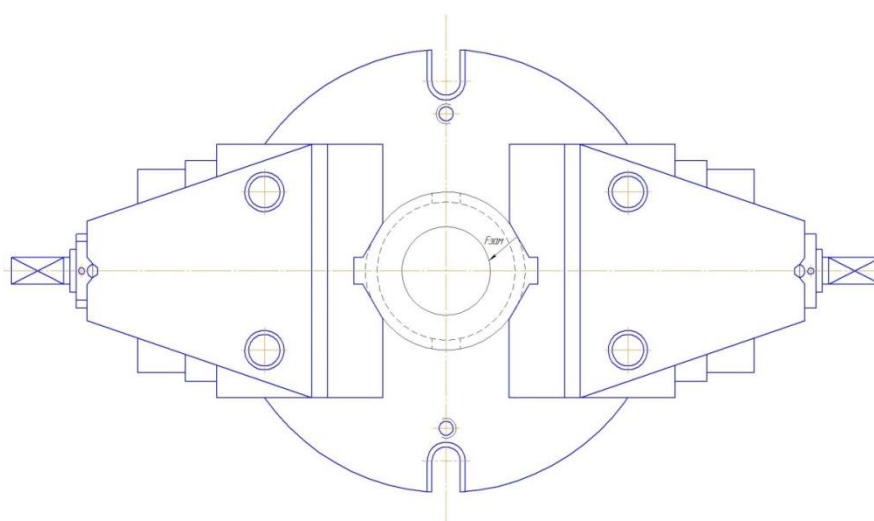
Принципиальная схема зажима заготовки в приспособлении с указанием мест приложения силы зажима.
